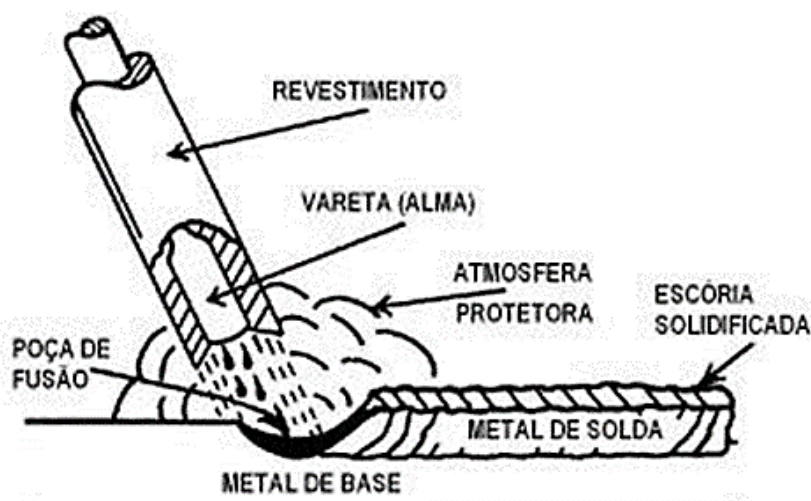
Ilustração da soldagem com eletrodo revestido. Fonte: FORTES, 2005
